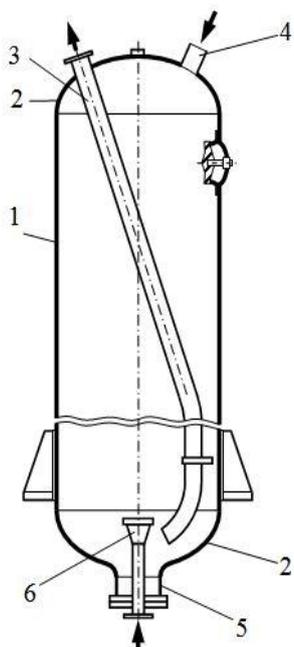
1 – корпус, 2 – сферические крышка и днище, 3 – разгрузочная труба, 4 – загрузочная труба, 5 – горловина, 6 – барботер (диспергатор)
